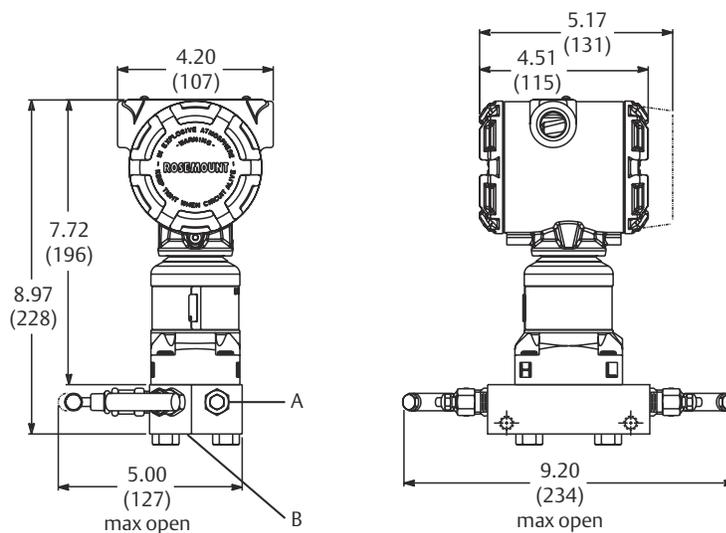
Копланарный клапанный блок модели 305 с двумя вентилями (в сборе с преобразователем давления 3051S_C)
